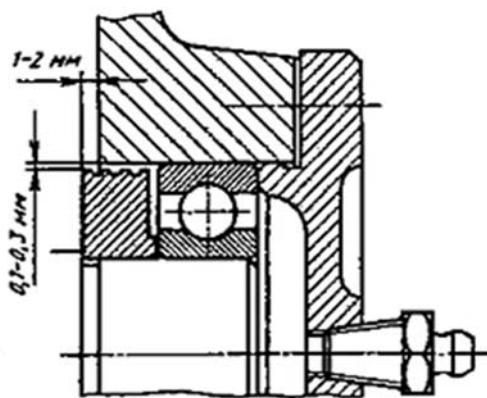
Подшипник, смазываемый пластичным смазочным материалом
